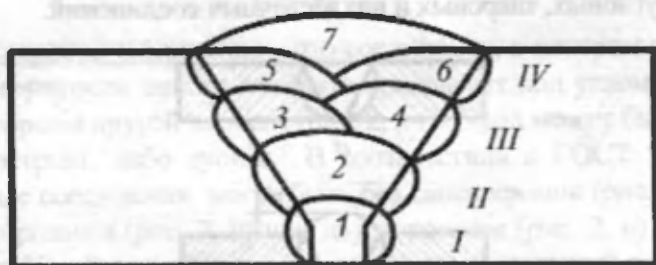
Многослойный сварной шов: 1-7 - последовательность выполнения переходов; I- IV - слои; 1 - корневой шов; 7 - облицовочный шов
